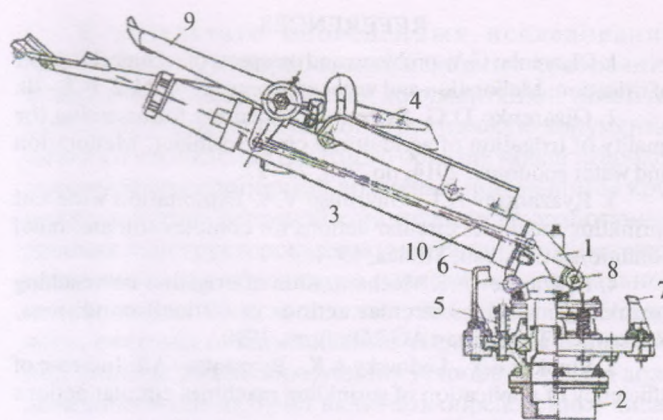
Схема дождевального аппарата ДМ-07.150: 1 – корпус; 2 – основание; 3 – ствол; 4 – лопатка вращения; 5 – механизм торможения; 6, 7 – копиры; 8 – ролик; 9 – лопатка реверсирования; 10 – тяга
